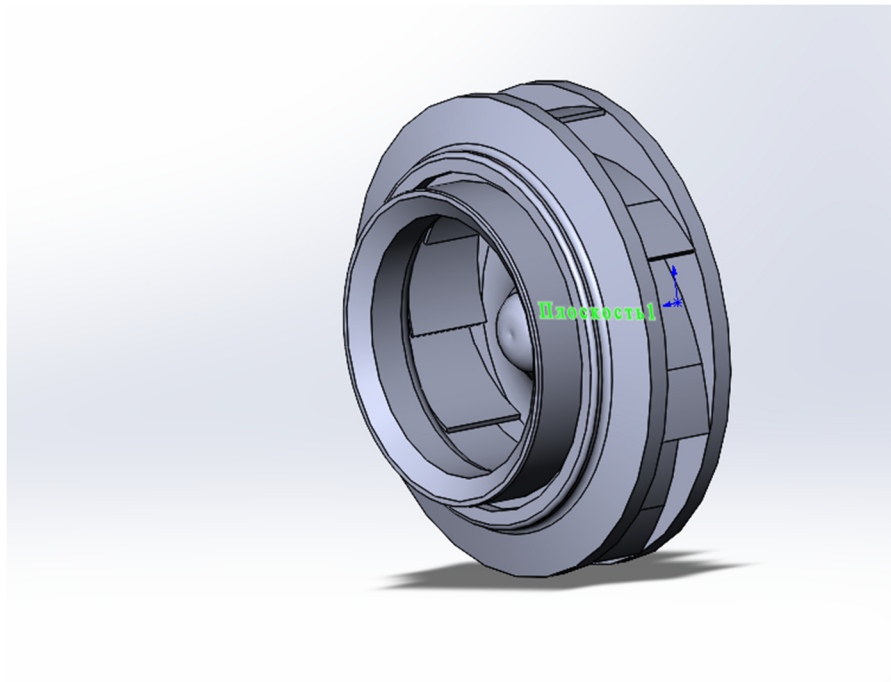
Повна 3D модель робочого колеса з лопатками
